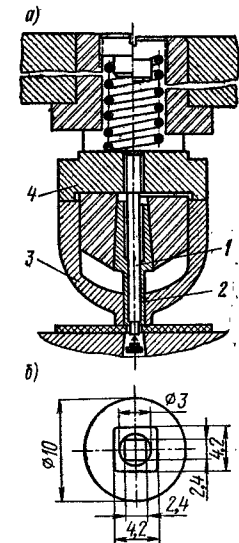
Штамп для пробивки и зачистки квадратных отверстий (а) и обрабатываемая деталь (б)
